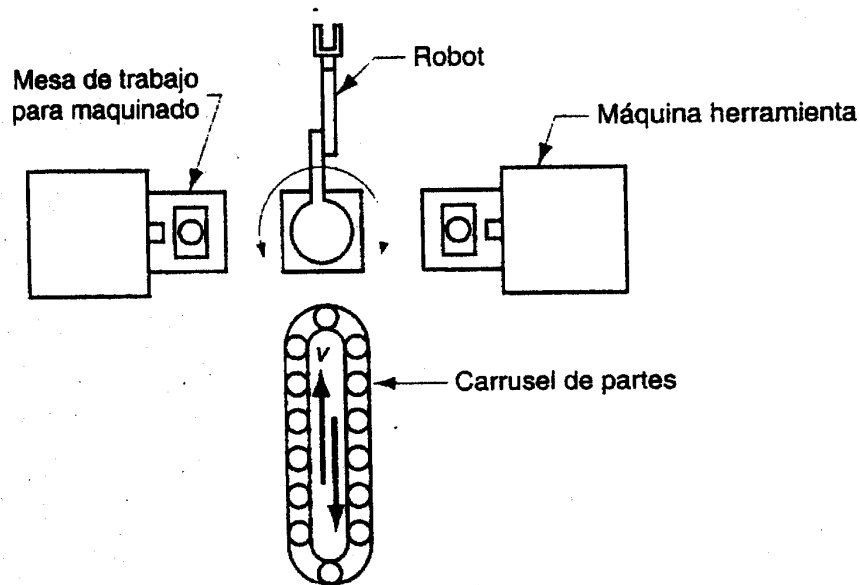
Distribución de planta de un FMS centrado en un robot.
